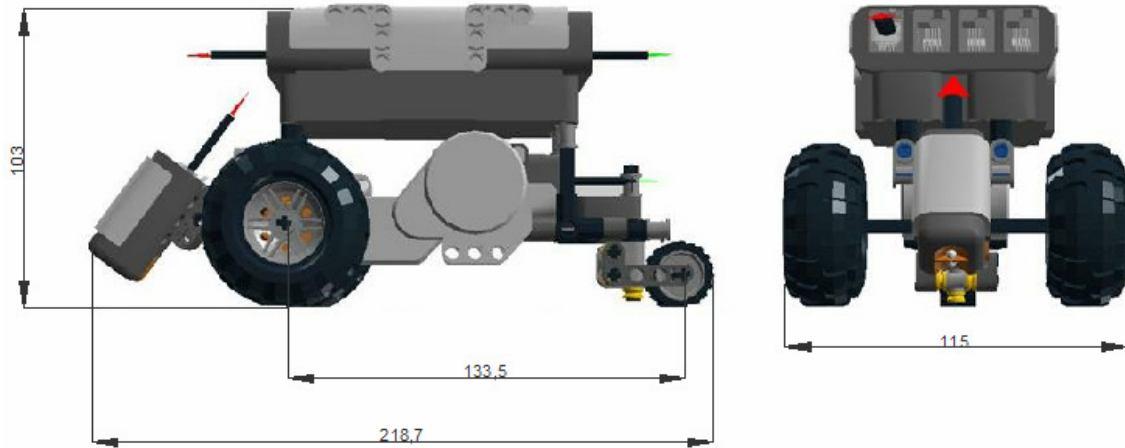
B.B3): Dimensiones del Primer montaje .
